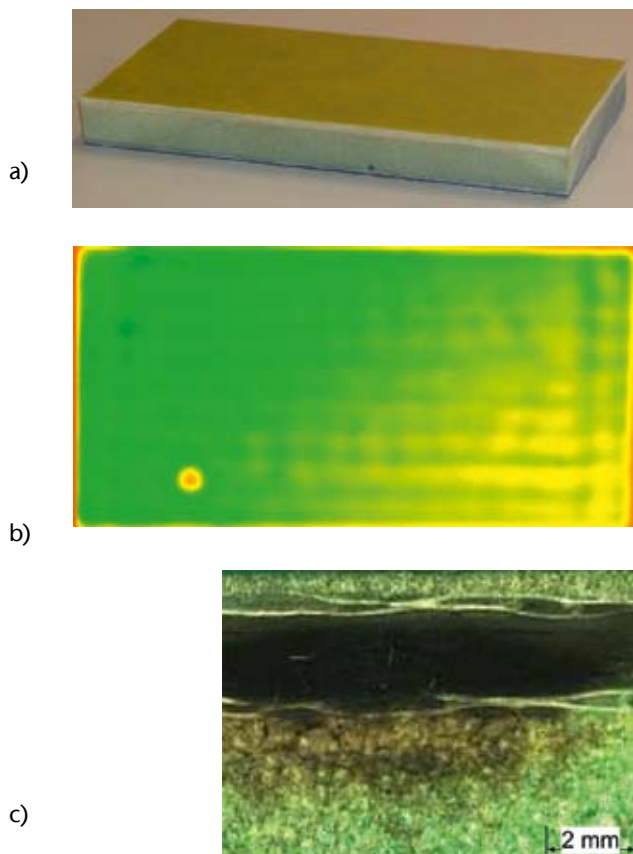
Sandwich GFK/ PVC-Schaum/ CFK mit Defekt: unzureichend harzgetränkte Glasfaserbündel.
